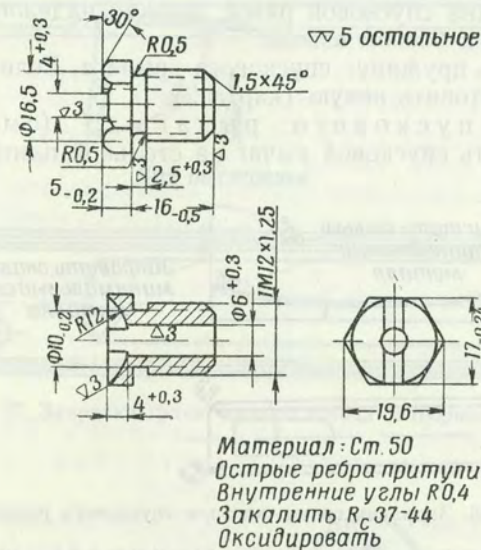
Винт (0-5) регулятора (первых годов изготовления)
